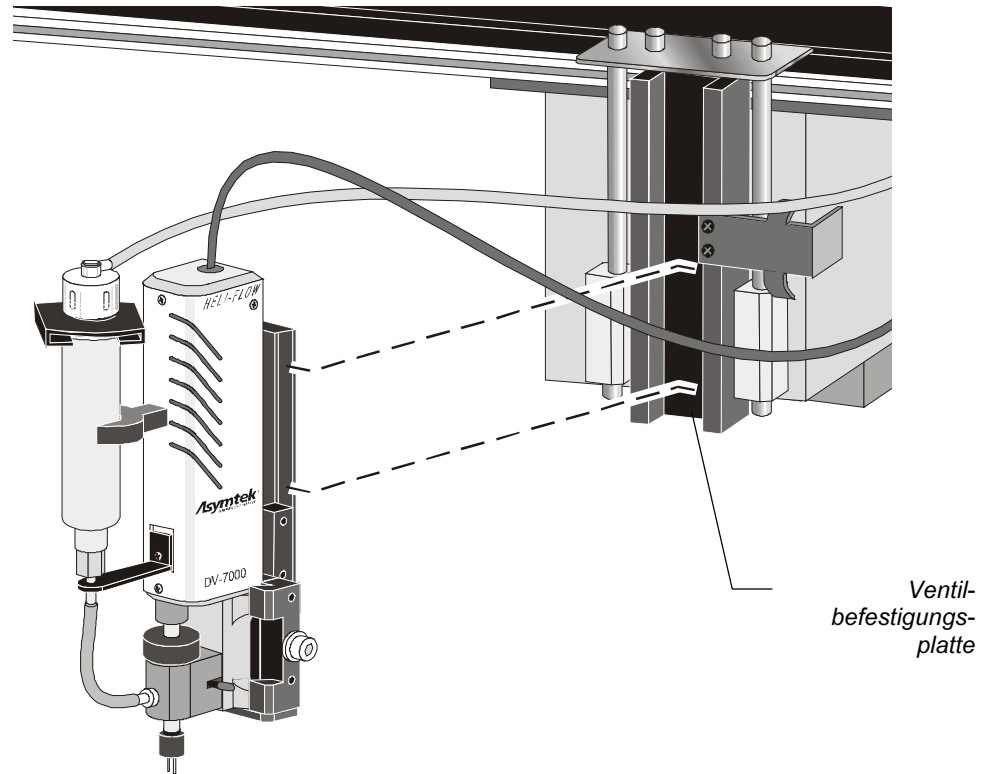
Befestigung des DV-7000 Montageteils (C-718-SMT)
